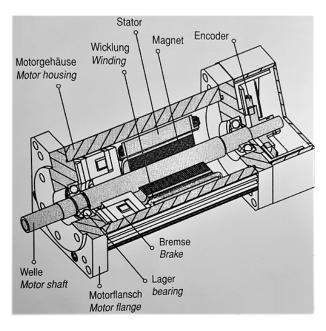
Schnittbild eines BLDC-Motors in Innenläuferausführung (Quelle: [2, S.75])
